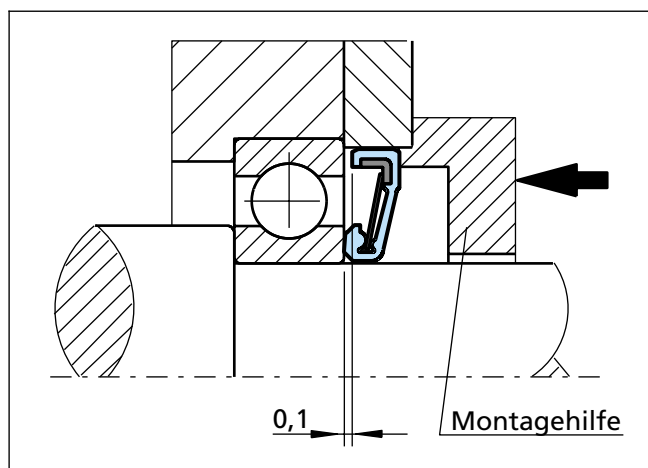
Einbau der Axial-Wellendichtung mit Montagehilfe
